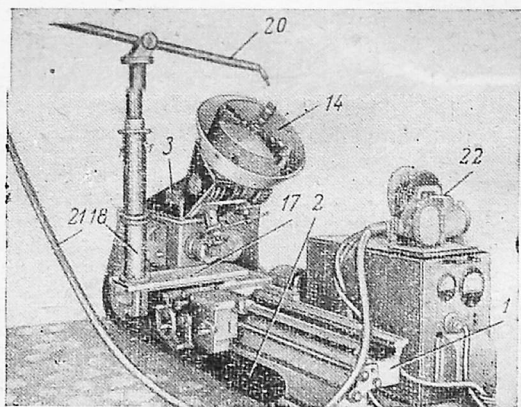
Универсальный сварочный станок, переделанный из небольшого токарного станка.
